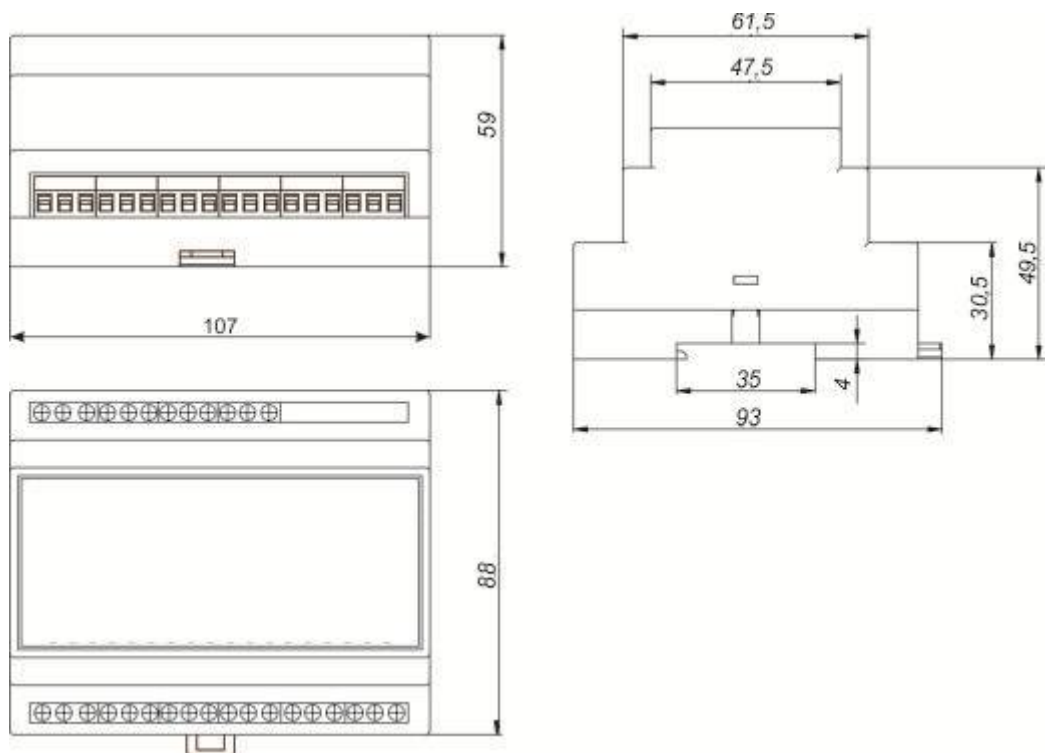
Габаритные размеры блока измерения РВ/12(24)УВ
